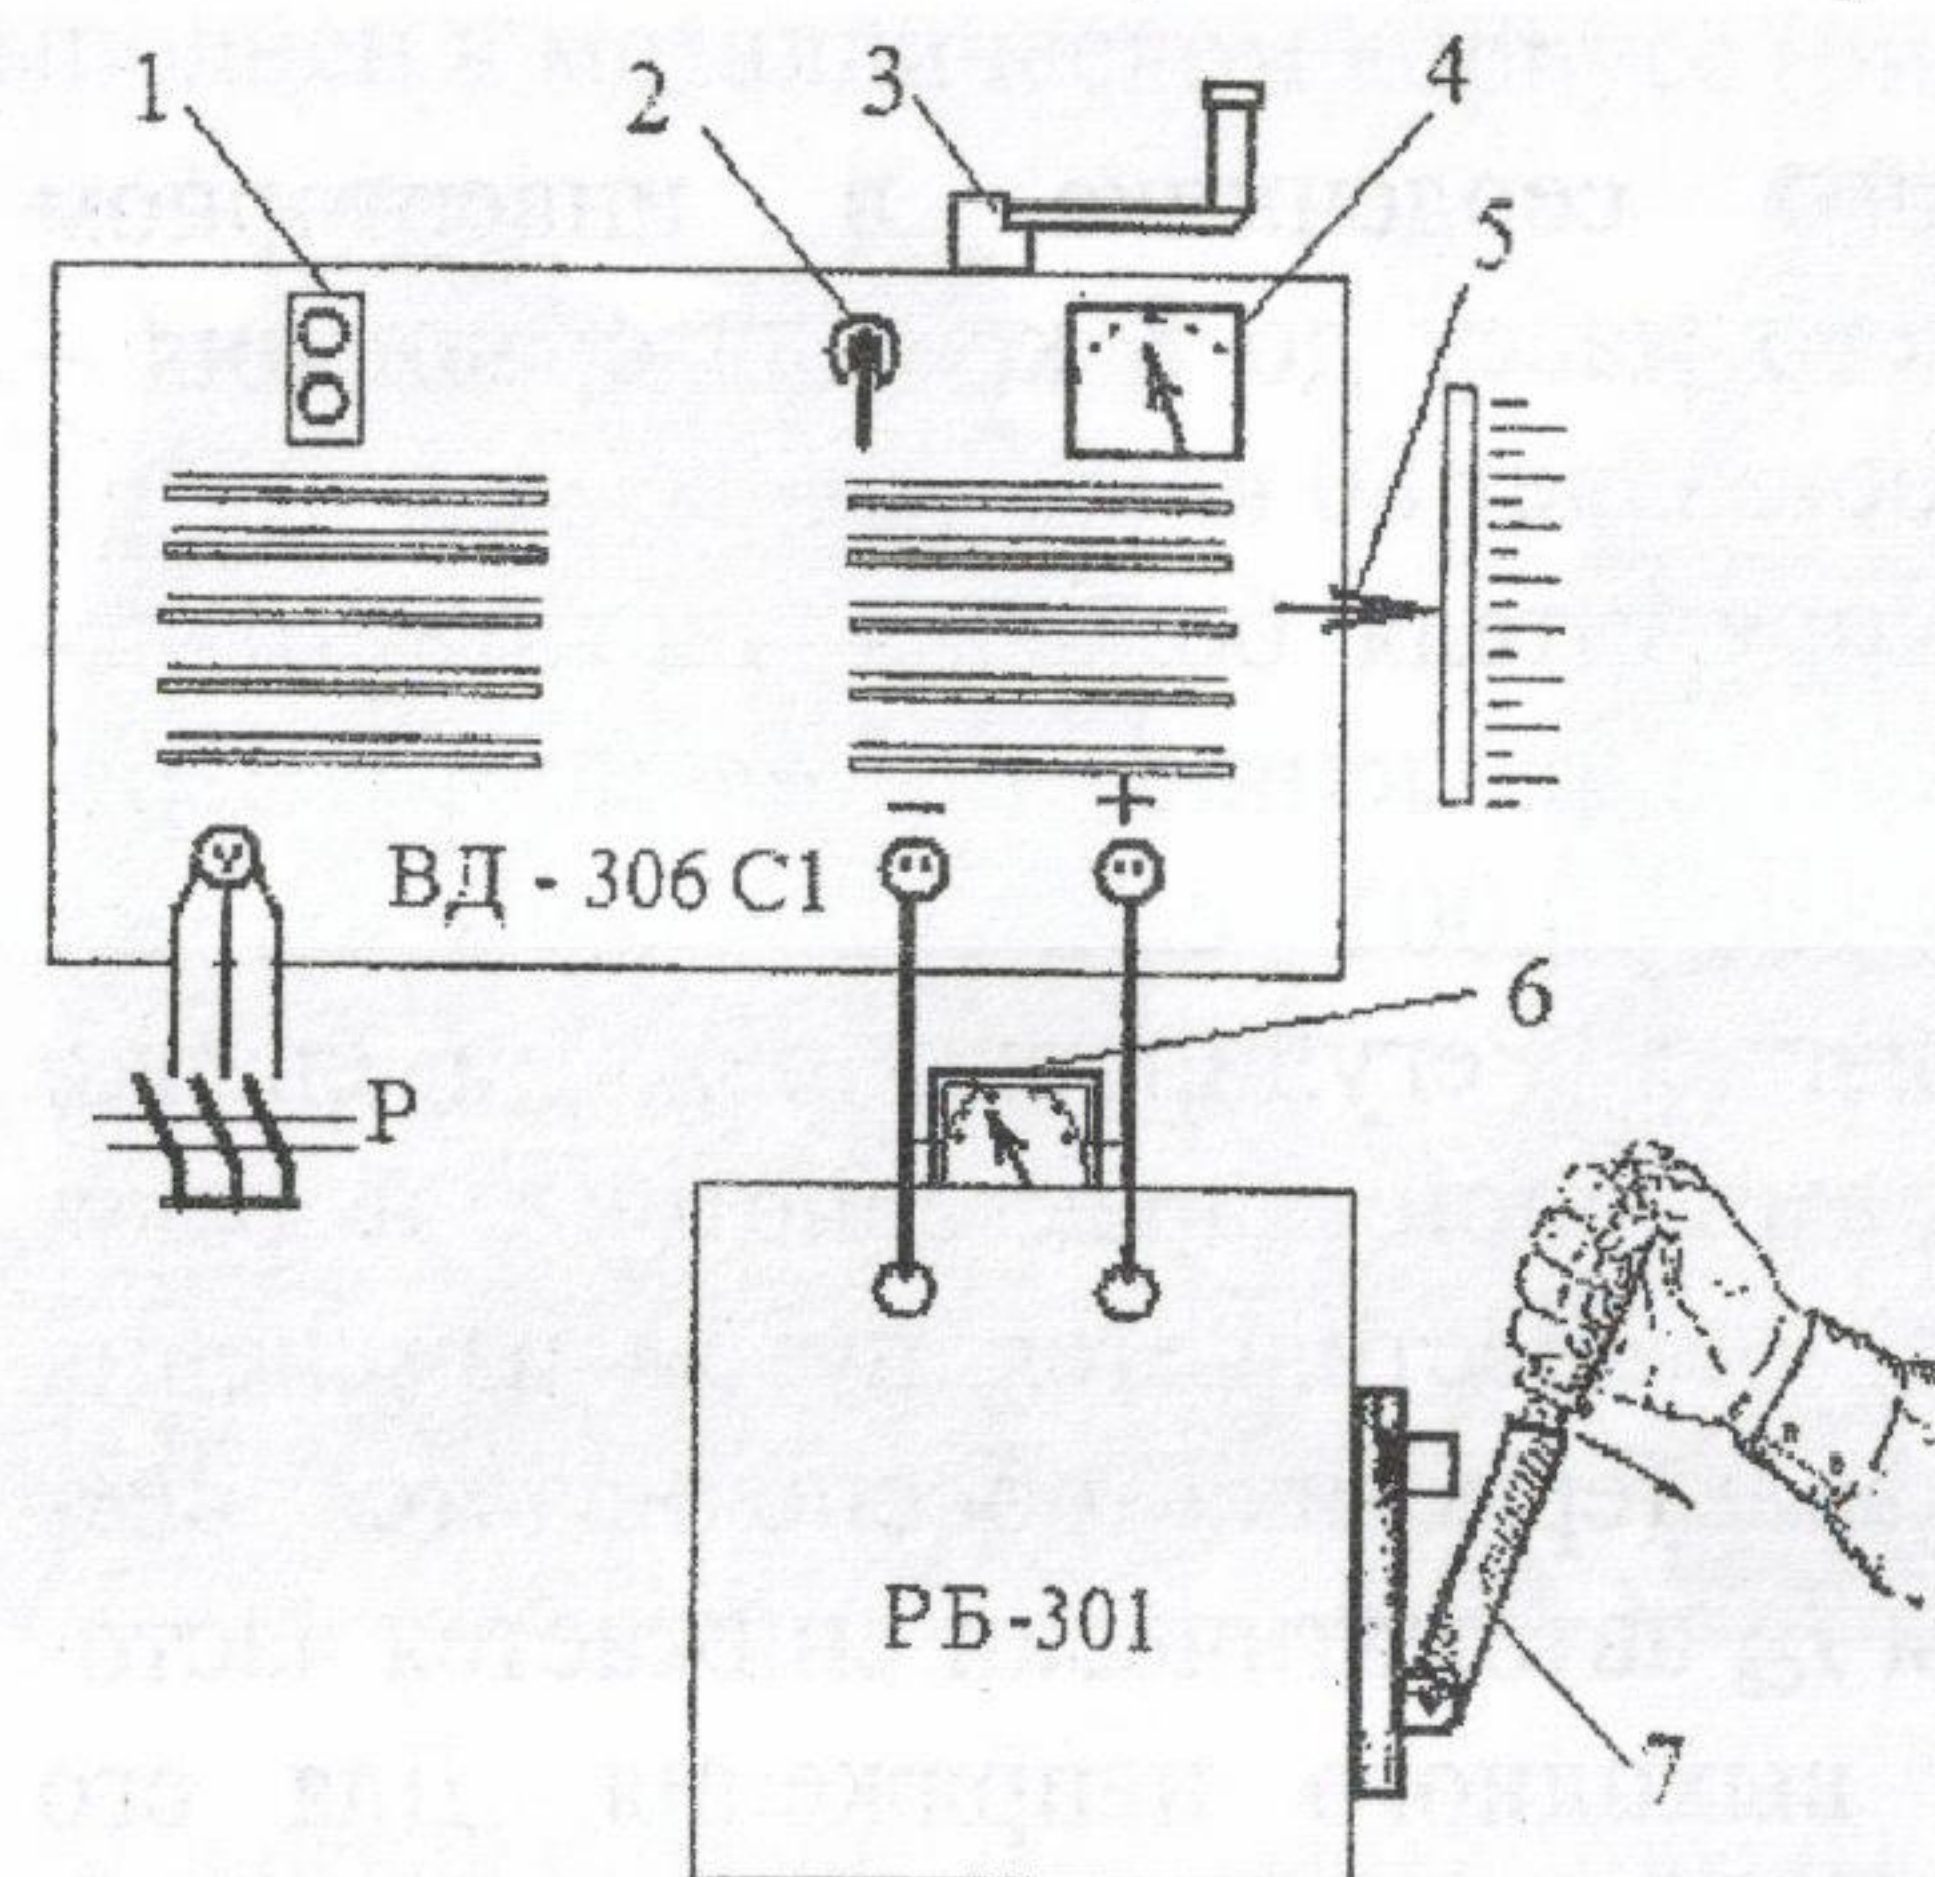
Схема опытной установки для определения внешней характеристики выпрямителя: 1-выключатель с кнопками «пуск» и «стоп»; 2 - переключатель ступеней тока; 3-рукоятка регулятора сварочного тока; 4 - амперметр; 5- указатель сварочного тока со шкалой; 6 - вольтметр; 7-контактный нож РБ-301
